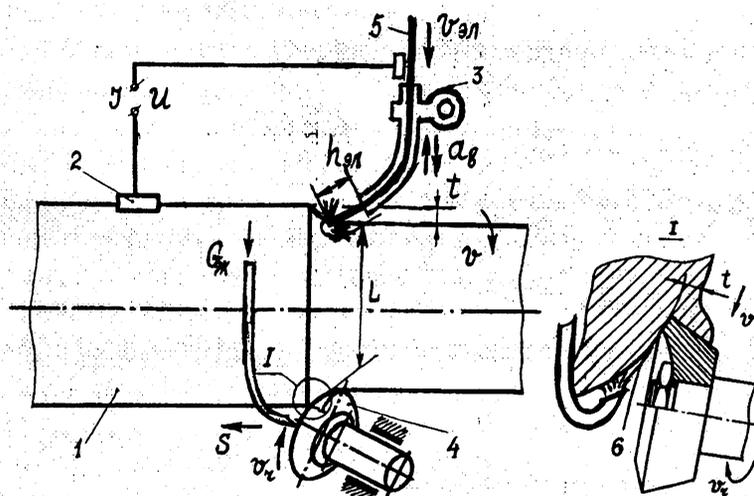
Наплавка проволоки с упрочняющим ротационным резанием: 1 – обрабатываемая деталь; 2 – скользящий контакт; 3 – мундштук наплавочной головки; 4 – ротационный резец; 5 – наплавочная проволока; 6 – охлаждающая жидкость; V – скорость главного движения; V_r – скорость дополнительного движения резца; S – скорость подачи; $V_{эл}$ – скорость подачи электродной проволоки; $h_{эл}$ – вылет электрода; $G_ж$ – расход жидкости; I – сила тока; U – напряжение дуги; t – глубина резания; L – расстояние от электрода до резца
